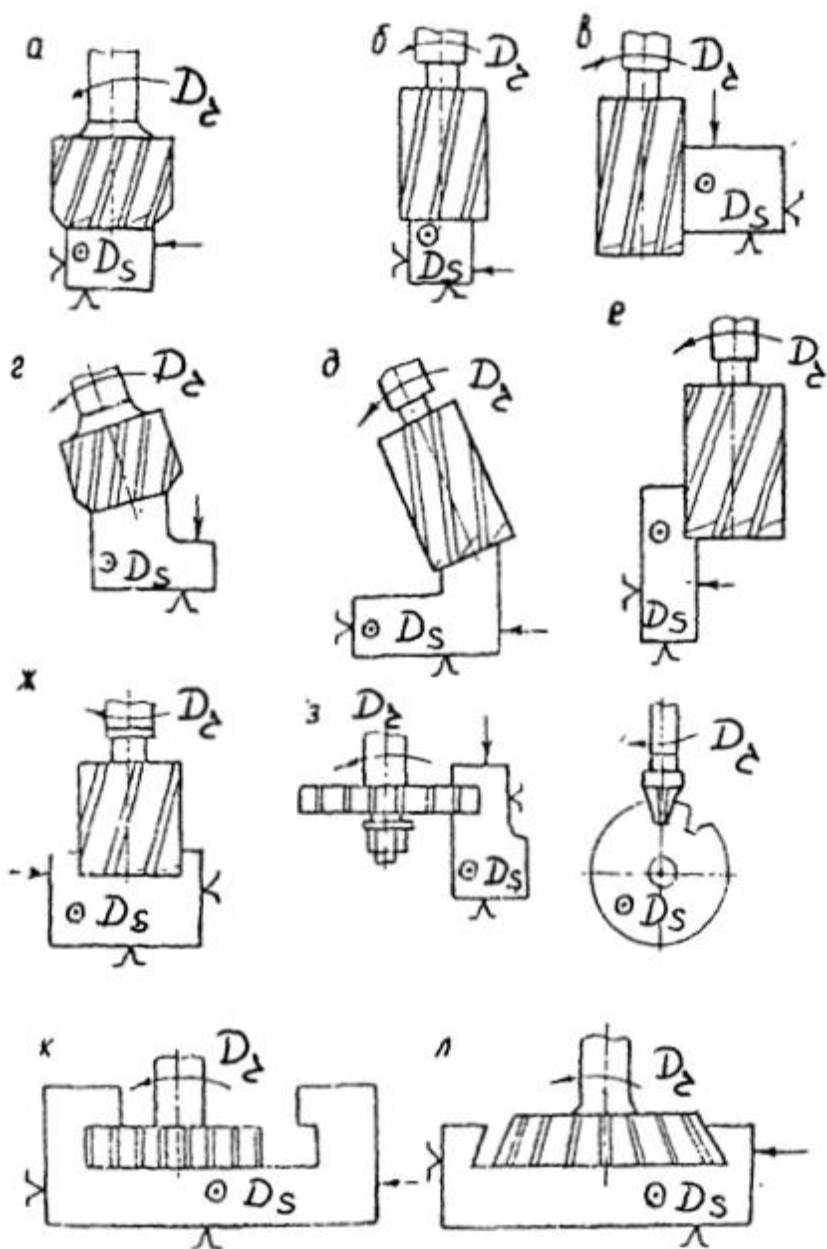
Схемы обработки поверхнонь на вертикально-фрезерных верстаках
